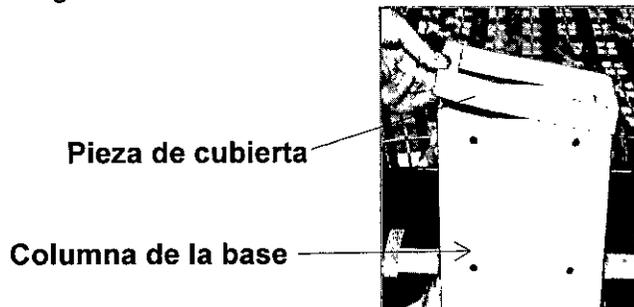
ARMADO DE LA BASE DE LA COLUMNA
